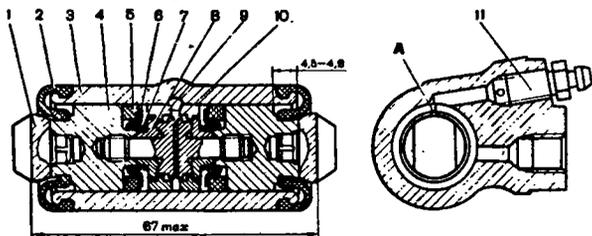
Колесный цилиндр: 1 - упор колодки; 2 - защитный колпачок; 3 - корпус цилиндра; 4 - поршень; 5 - уплотнитель; 6 - опорная чашка; 7 - пружина; 8 - сухари; 9 - упорное кольцо; 10 - упорный винт; 11 - штуцер; А - прорезь на упорном кольце
